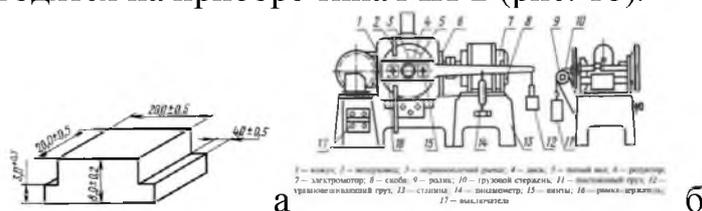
а) форма и размеры образца для испытания на приборе МИ-2; б) прибор типа МИ-2
